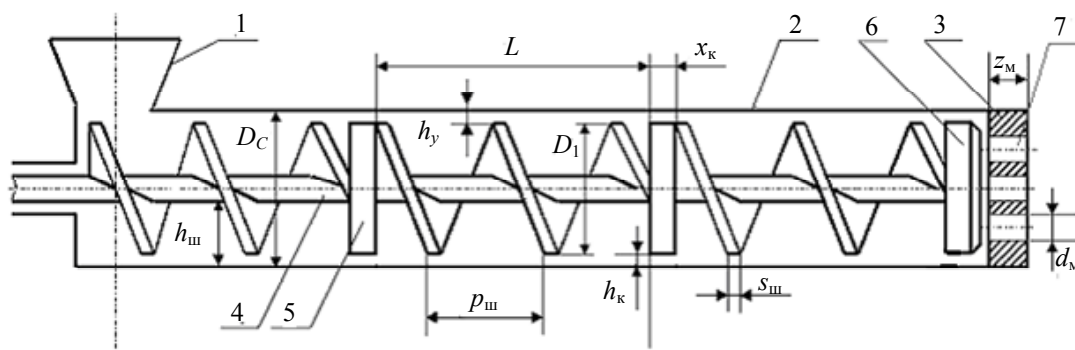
Схема прессующего механизма: 1 – загрузочное устройство; 2 – шнековый цилиндр; 3 – матрица; 4 – шнек; 5 – компрессионный затвор; 6 – головка экструдера; 7 – фильера
